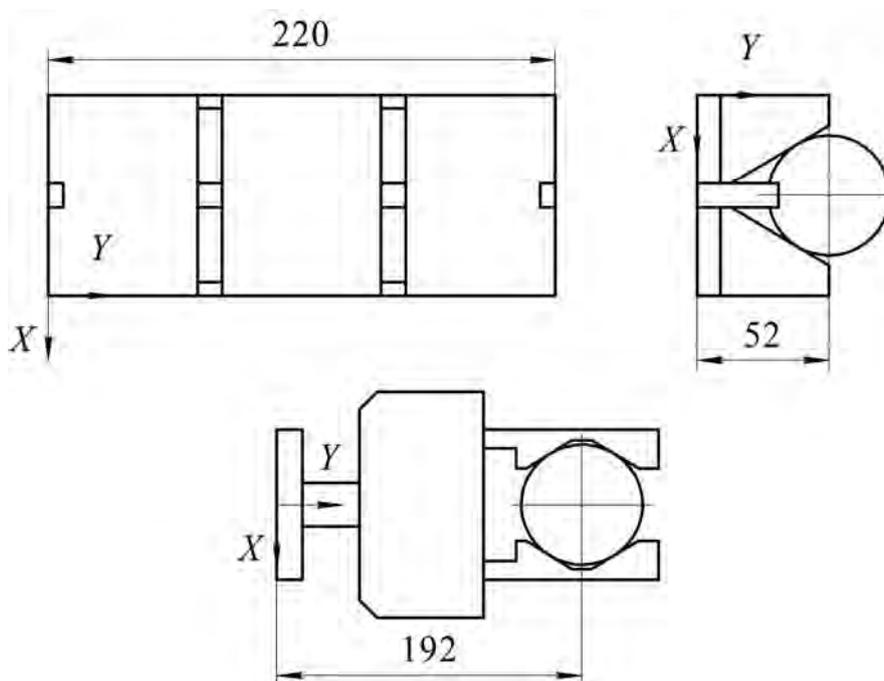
Положение заготовки при создании рабочей системы координат
